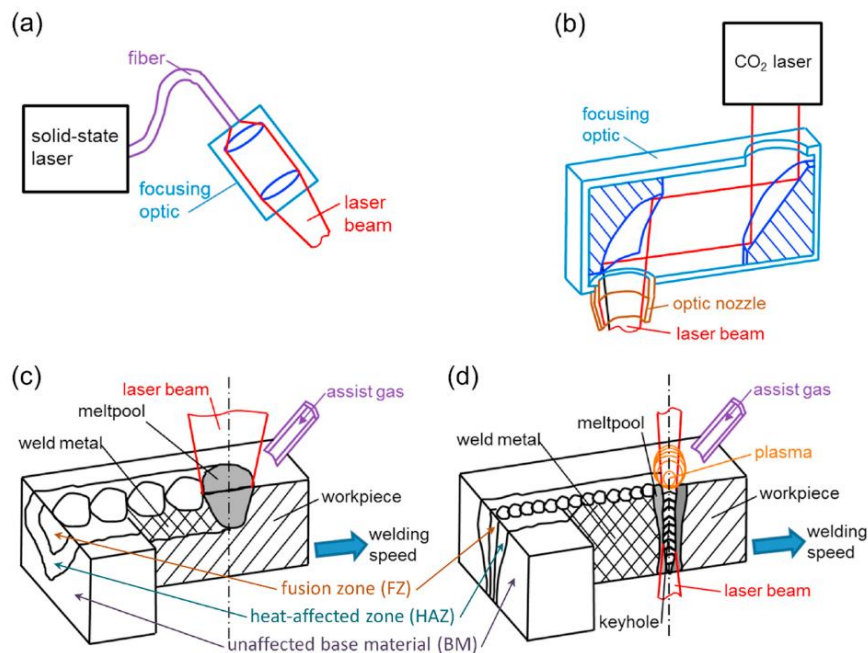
Principe du LBW : (a) Laser à l'état solide, (b) Laser CO₂, (c) Soudage par conduction thermique, (d) Soudage par trou de serrure [10].
